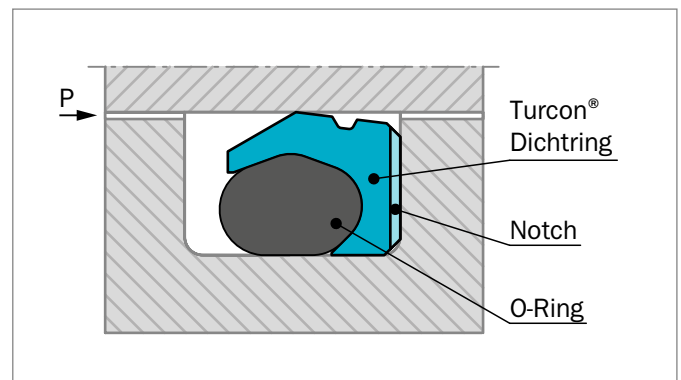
Turcon® Roto VL Seal® mit Radial-Notch
